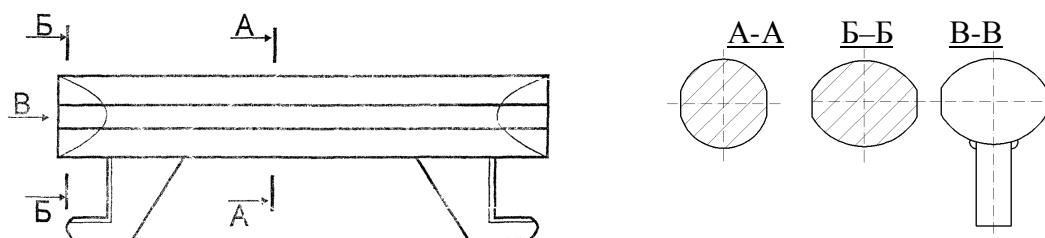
Колосник [11], изготовленный методами прокатки верхней части и сварки с нижней частью
